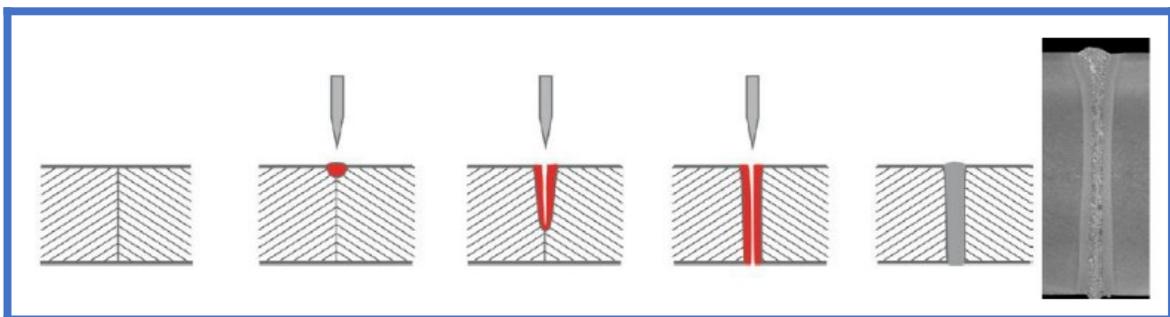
Efecto de penetración profunda: La fusión y la vaporización permiten que el haz de electrones penetre el material profundamente. El baño de soldadura (weld pool) penetra en la pieza de trabajo. Derecha: Micrografía de una soldadura de penetración completa en acero S355 de espesor 50 mm.
